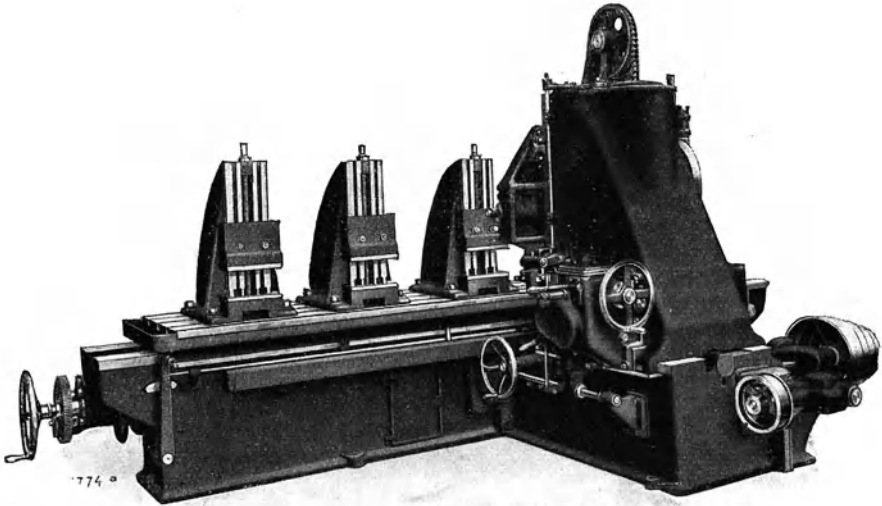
Die Zahnstangenfräsmaschine von J. E. Reinecker.
